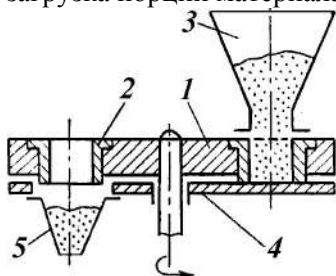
Дисковый дозатор с мерными цилиндрами: 1 – диск; 2 – мерный цилиндр; 3 – бункер; 4 – неподвижный стол; 5 – направляющая воронка.
